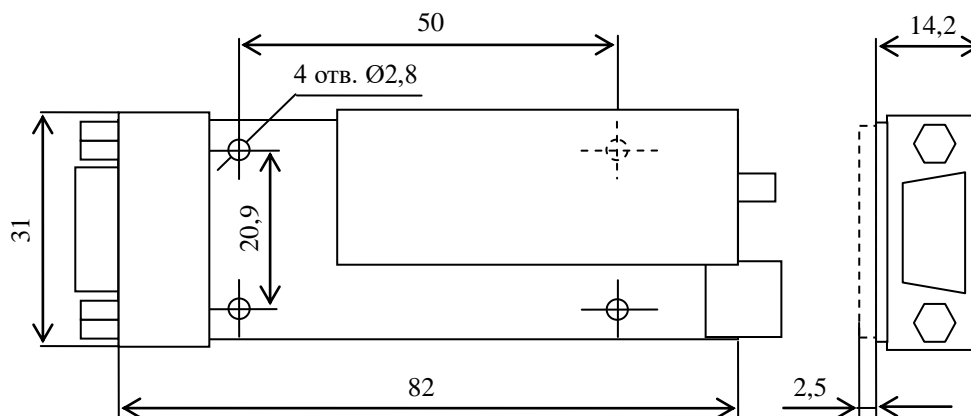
Габаритный чертёж бескорпусного варианта радиомодема РМД400-1-УР0
